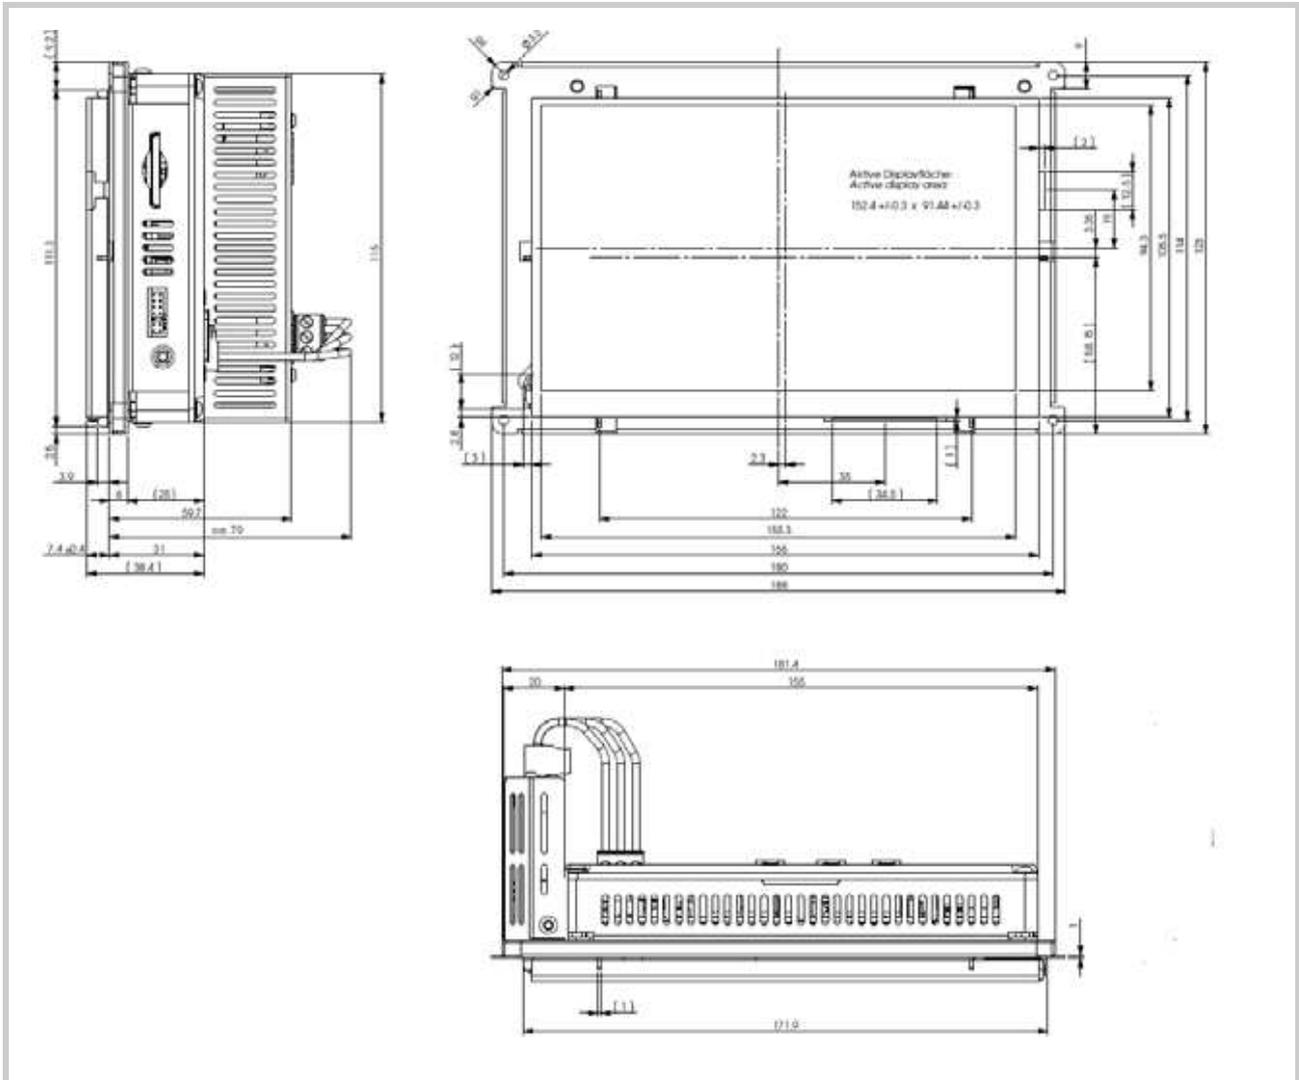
Mechanische Abmessungen der 7,0"-Geräte in mm
